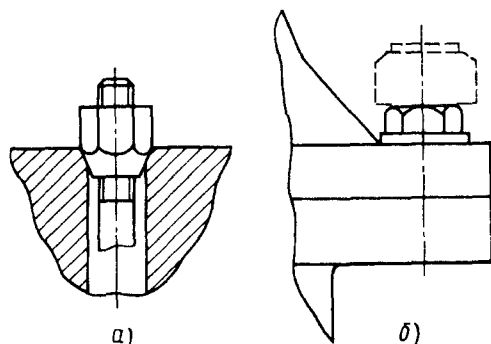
Примеры конструктивных решений, повышающих технологичность сборки резьбовых соединений
